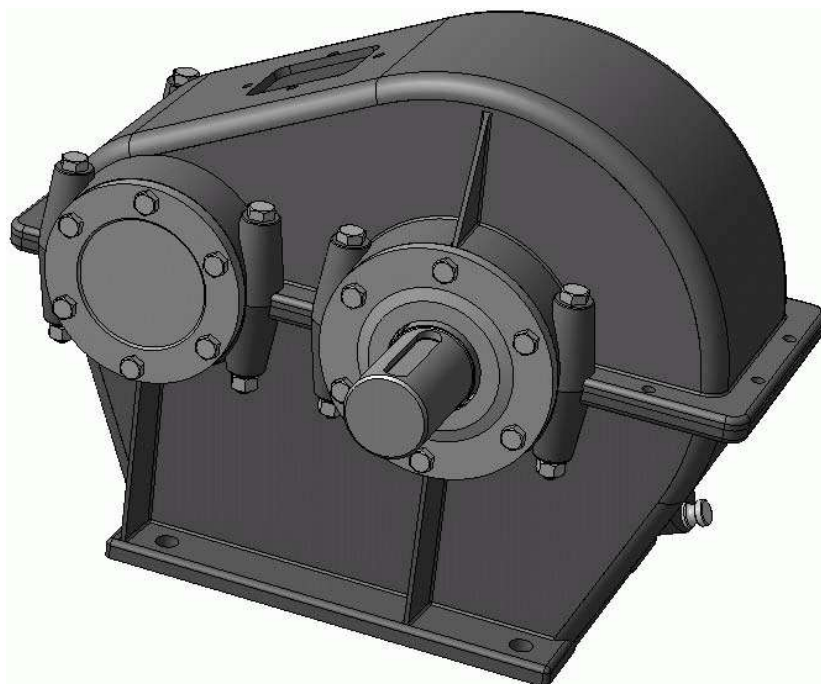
Соединение болтами бобышек крышки и корпуса редуктора с помощью команды Массив по сетке
